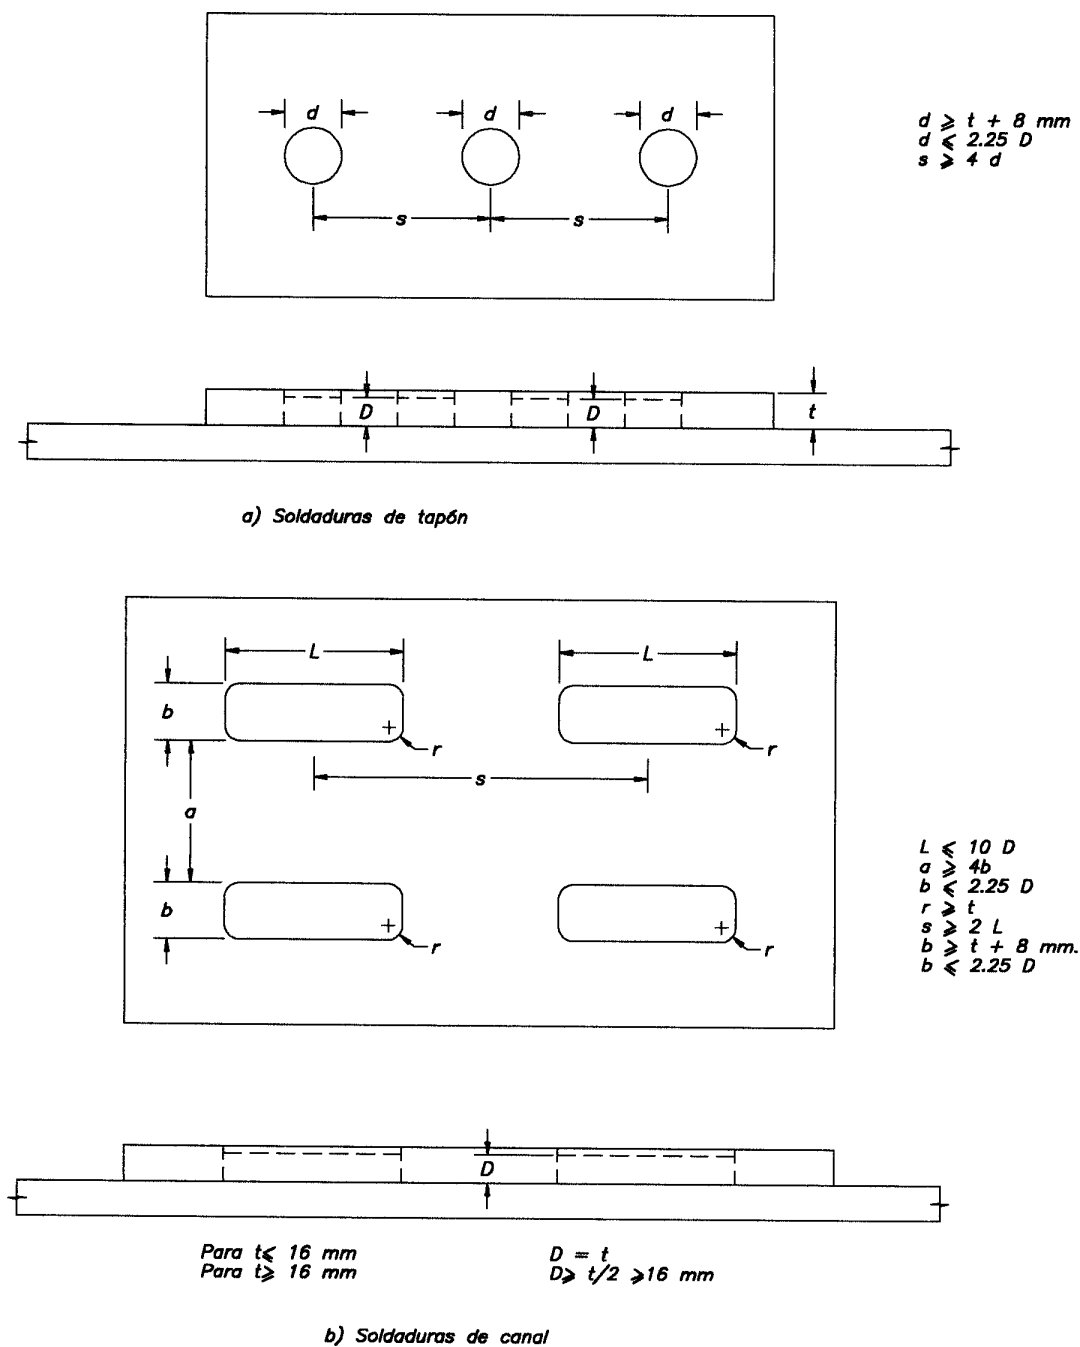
Requisitos para soldaduras de tapón o canal.
